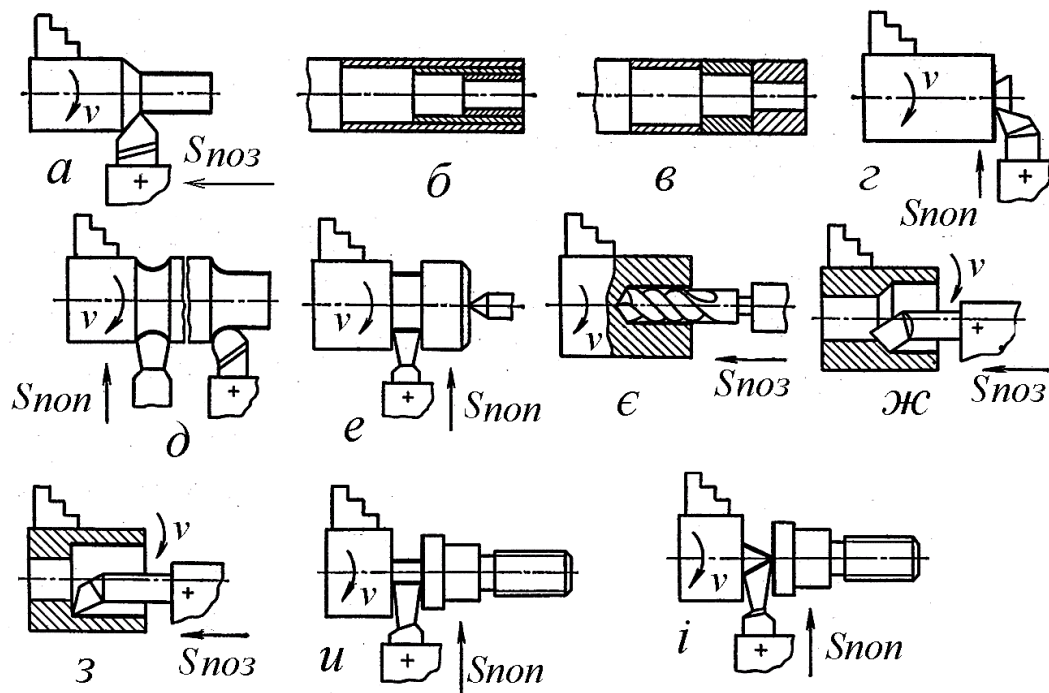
Схеми обробки заготовок на токарних верстатах
